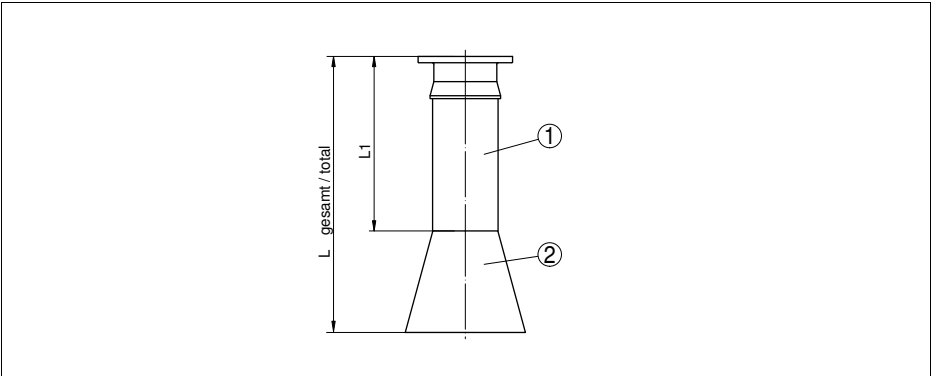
Prolongamento como peça única, com antena tipo corneta soldada, medidas de acordo com as especificações da encomenda
